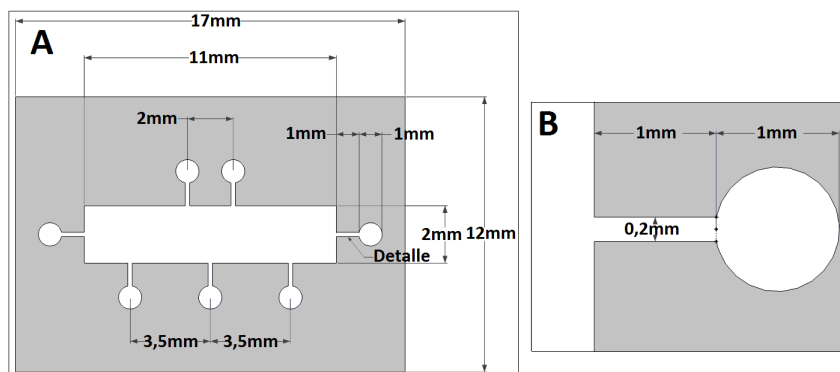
Plano de la máscara de acero. A: Máscara completa B: Detalle
